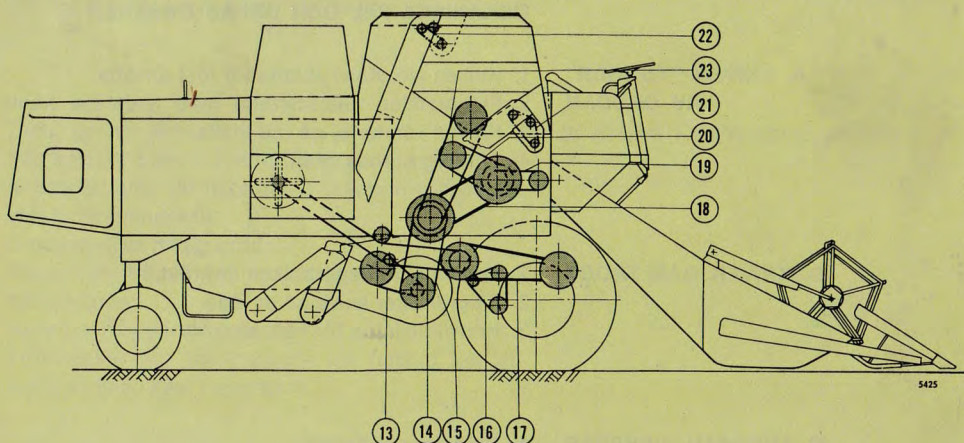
Remdrift för skördetröska i tankutförande (höger sida).
